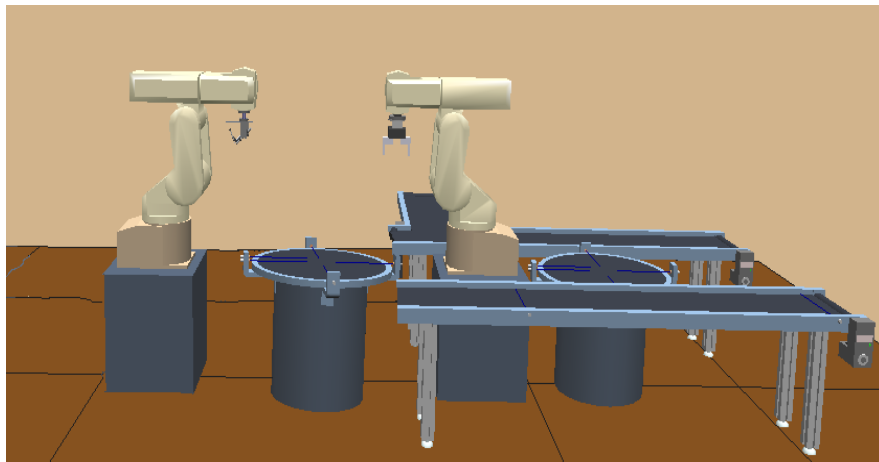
Simulación del sistema del proceso del Ensamblaje y Soldadura de la tarjeta impresa, vista de frente (Cambio de la planta).
